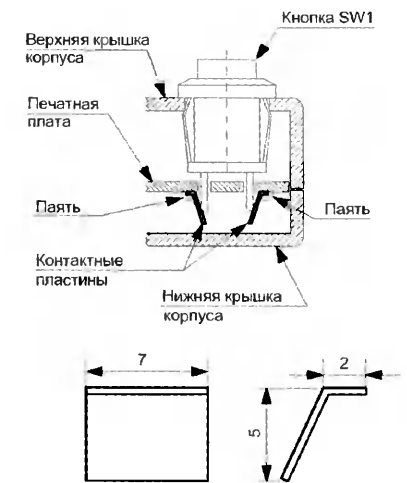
Установка кнопки SW1 и чертеж контактной пластины
